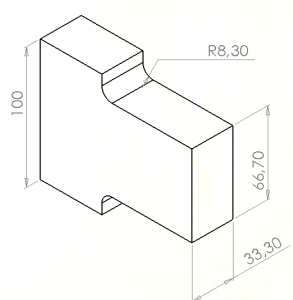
16 - Dimensões geométricas do detalhe estrutural. Dimensões em [mm].
